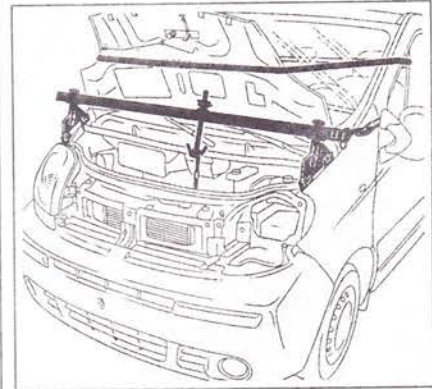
Установите опорную перекладку для вывешивания двигателя Mot. 1453 и приспособление Mot. 1453-01.
